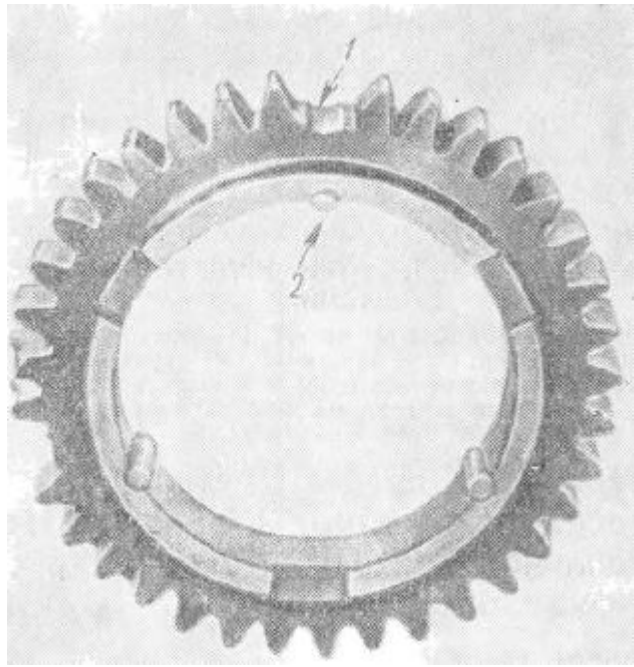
Втомна поломка (відмічена стрілкою 1) зуба цементованого і загартованого колеса обумовлена підвищеним натягом циліндричної шпонки 2 в з'єднанні даного колеса з другим.
